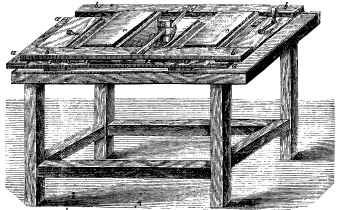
Th. Rißbüttle Steinbleif-Maschine.
